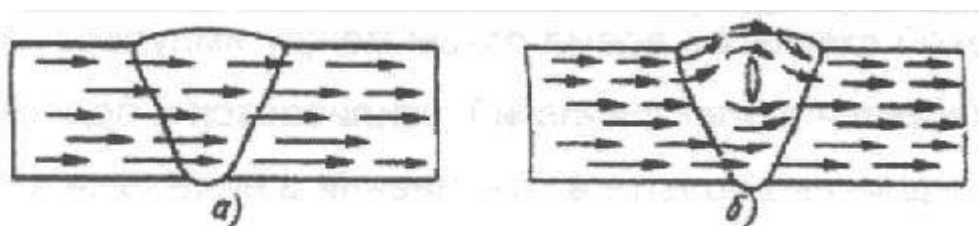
Прохождение магнитного силового потока по сварочному шву:
